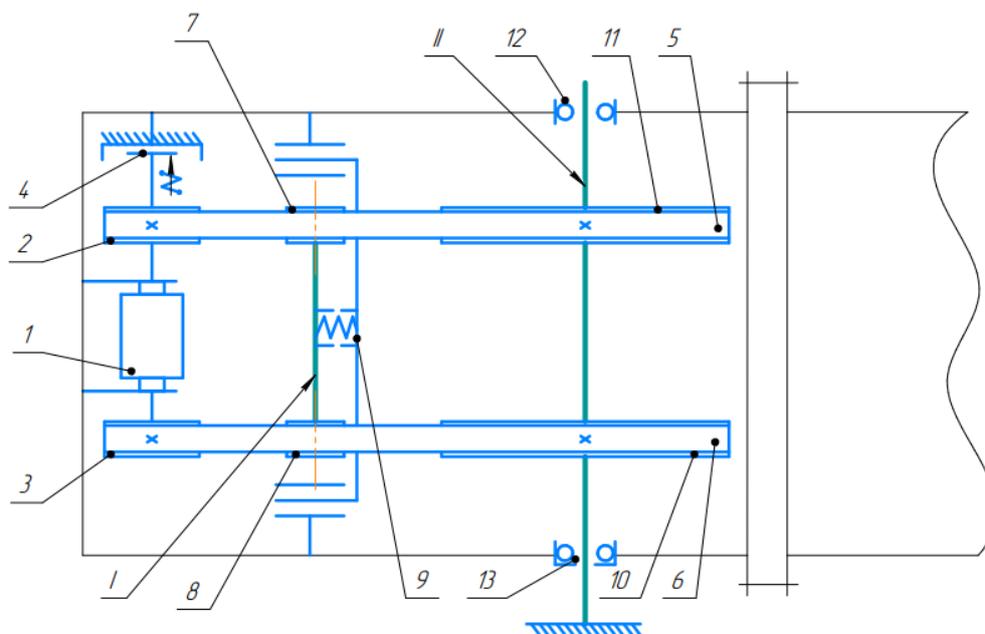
Привод поворотный принципиальная кинематическая схема вариант с зубчато-ременной передачей.
